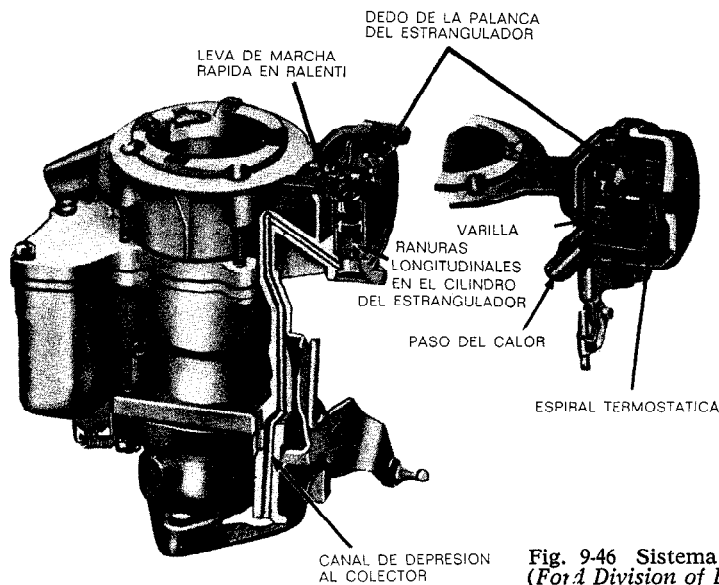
Sistema de estrangulador automático en un carburador (Ford Division of Ford Motor Company).
